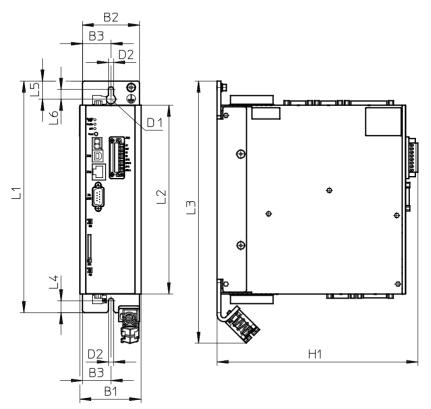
Motorcontroller CMMP-AS-...-M0: Montageplatte
